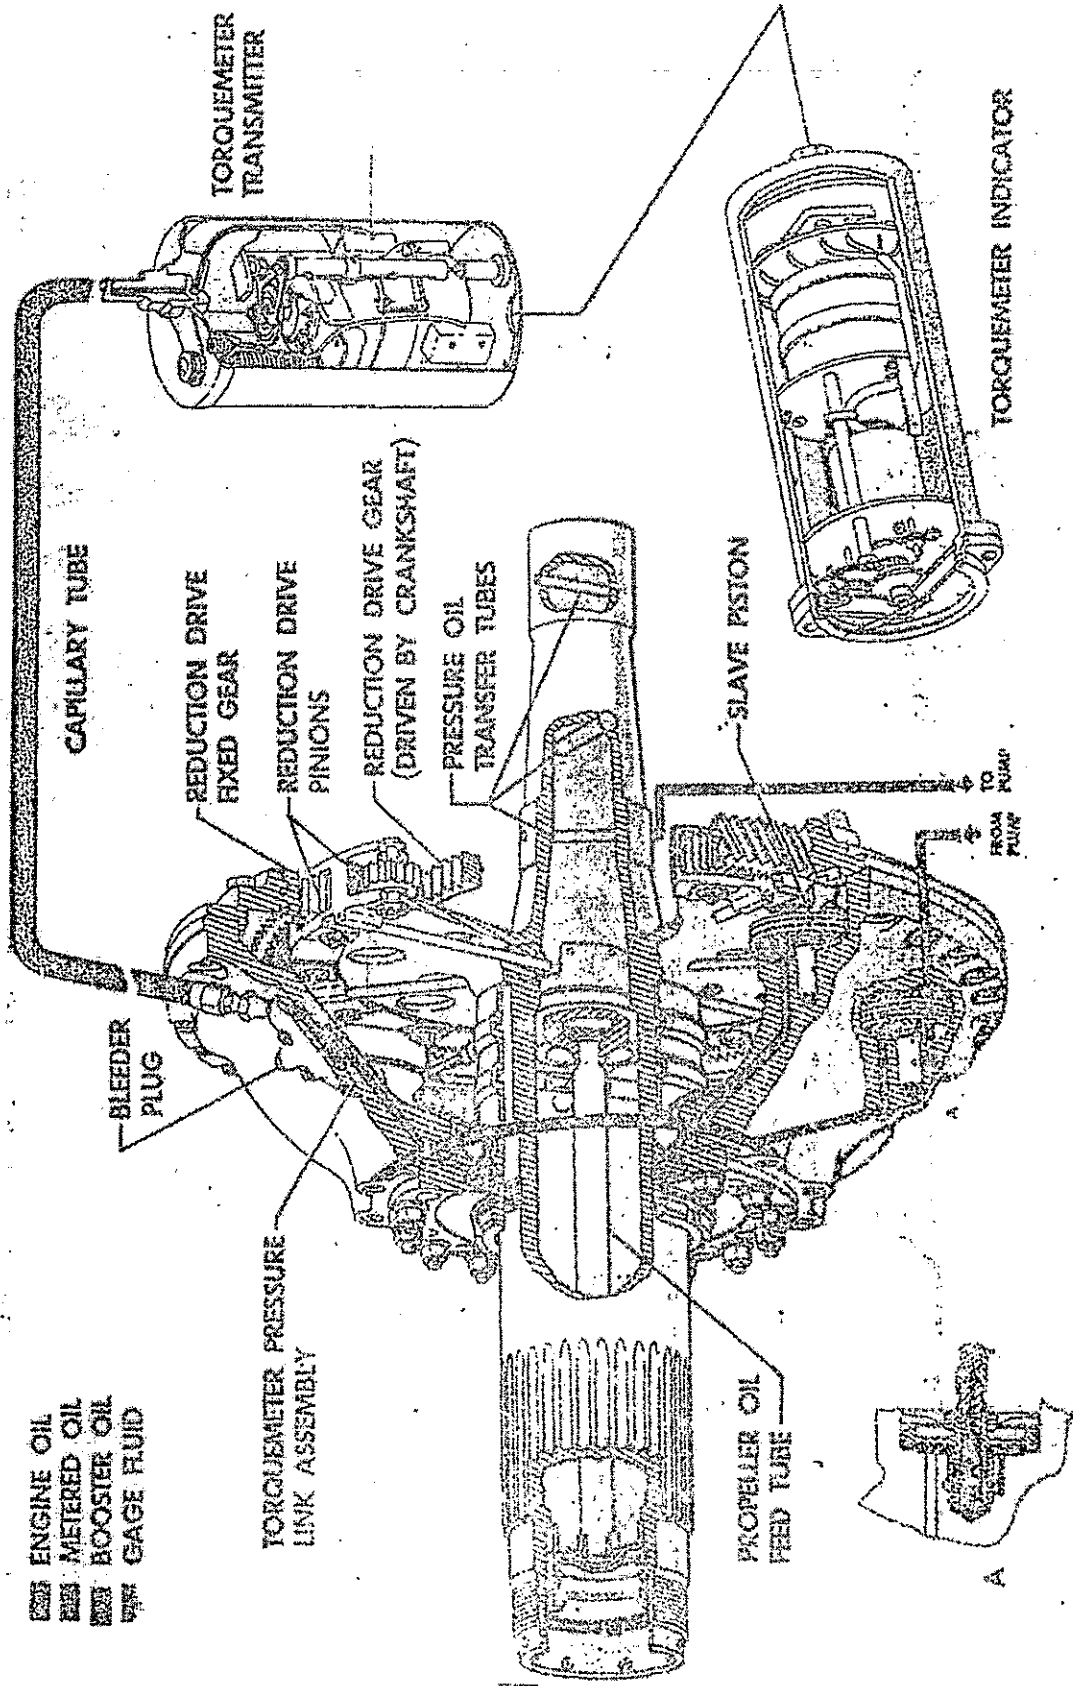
REDUCTION FIXED GEAR หมายเลข ๕
